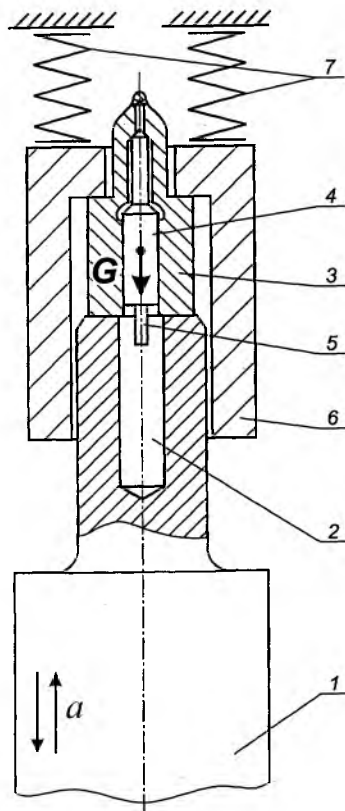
Устройство для разборки распылителя форсунки: 1 – торец трансформатора амплитуды продольных колебаний (концентратор); 2 – отверстие; 3 – корпус распылителя форсунки; 4 – иглы распылителя форсунки; 5 – хвостовик иглы; 6 – упор; 7 – винтовые пружины
